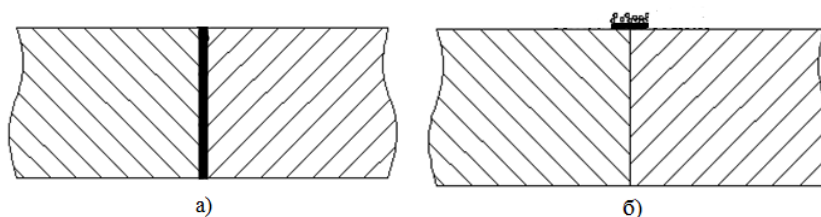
Методы ввода присадочного материала в зону сварного шва
